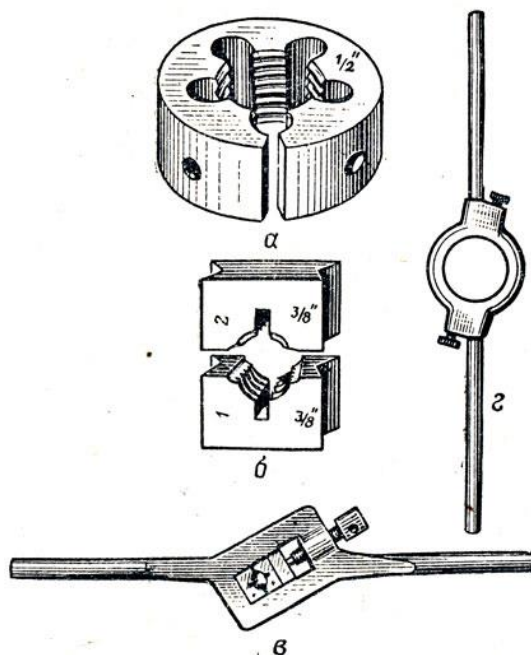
Плашки: а - круглая плашка; б - раздвижная плашка (или клупповая); в - клупп; г - вороток
